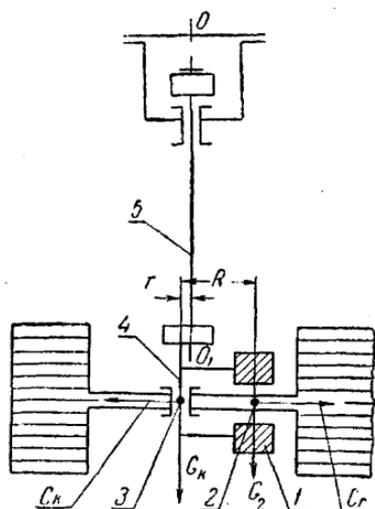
Схема приводного механизма самобалансирующегося отсева с жестким приводным валом.
